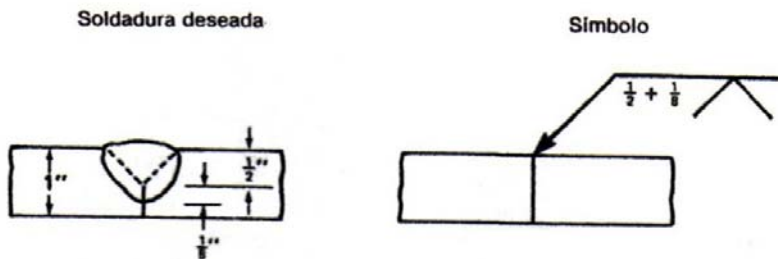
Símbolo de soldadura con especificación de la penetración en la raíz.
